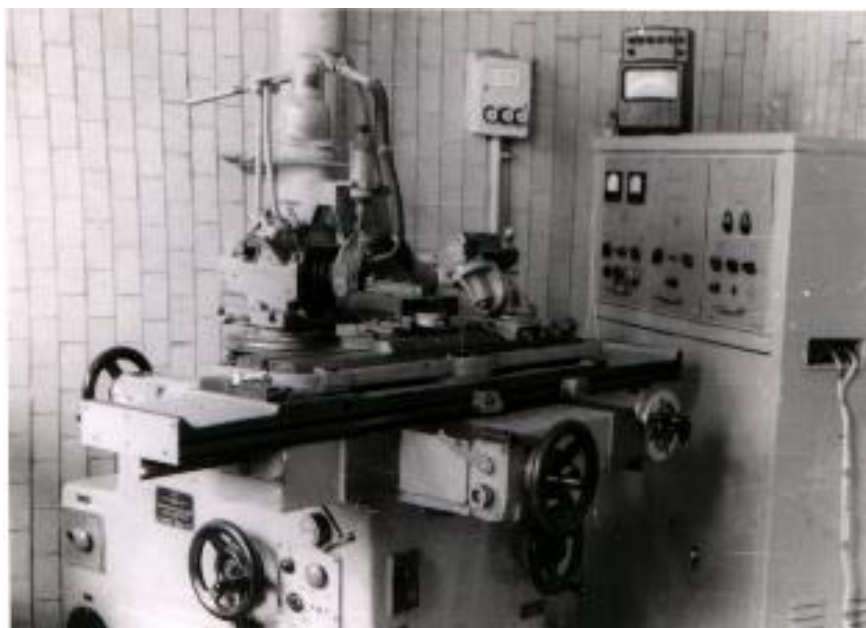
Общий вид установки и схема модернизации станка для АИШ:
